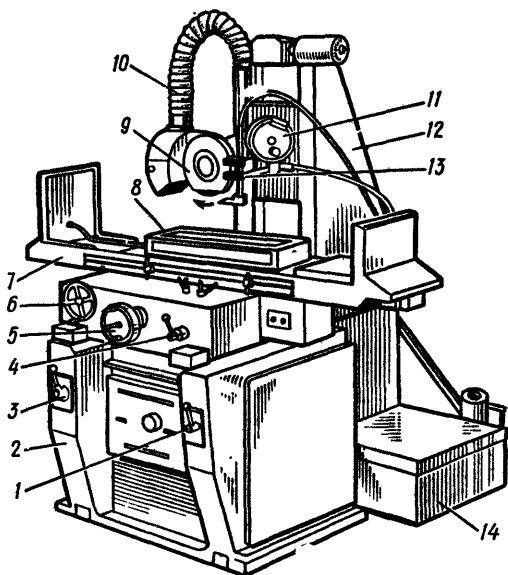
Плоскошлифовальный станок ЗБ71М: 1 — рычаг, 2 — станина, 3 — устройство для вертикального перемещения шлифовальной бабки, 4 — устройство для переключения магнитной плиты, 5 — устройство для ручного переключения поперечной подачи, 6 — маховик, 7 — стол, 8 — магнитная плита, 9 — кожух, 10 — устройство для отсоса абразивной пыли, 11 — микрометрическая вертикальная подача, 12 — колонка, 13 — шлифовальная бабка, 14 — гидропривод
